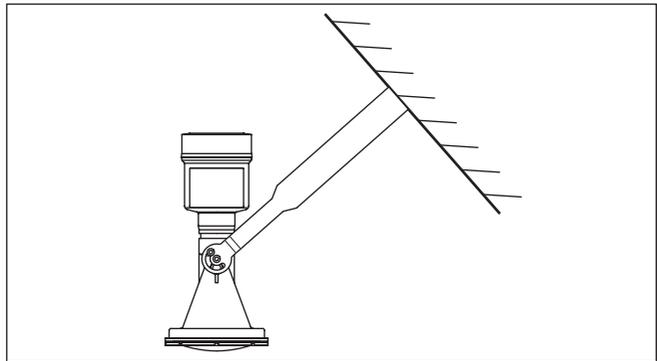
Montage mural pour mur en pente via l'étrier de montage avec une longueur de 300 mm
